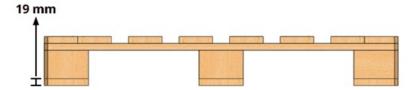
Esquema de vista lateral de um pallet com tábuas inferiores de 19 mm de espessura.
